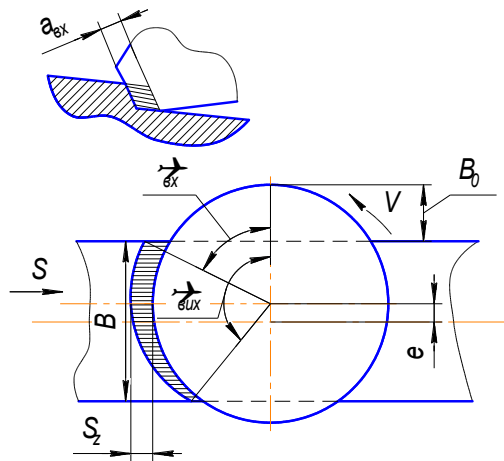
Схема розташування фрези відносно оброблюваної поверхні
